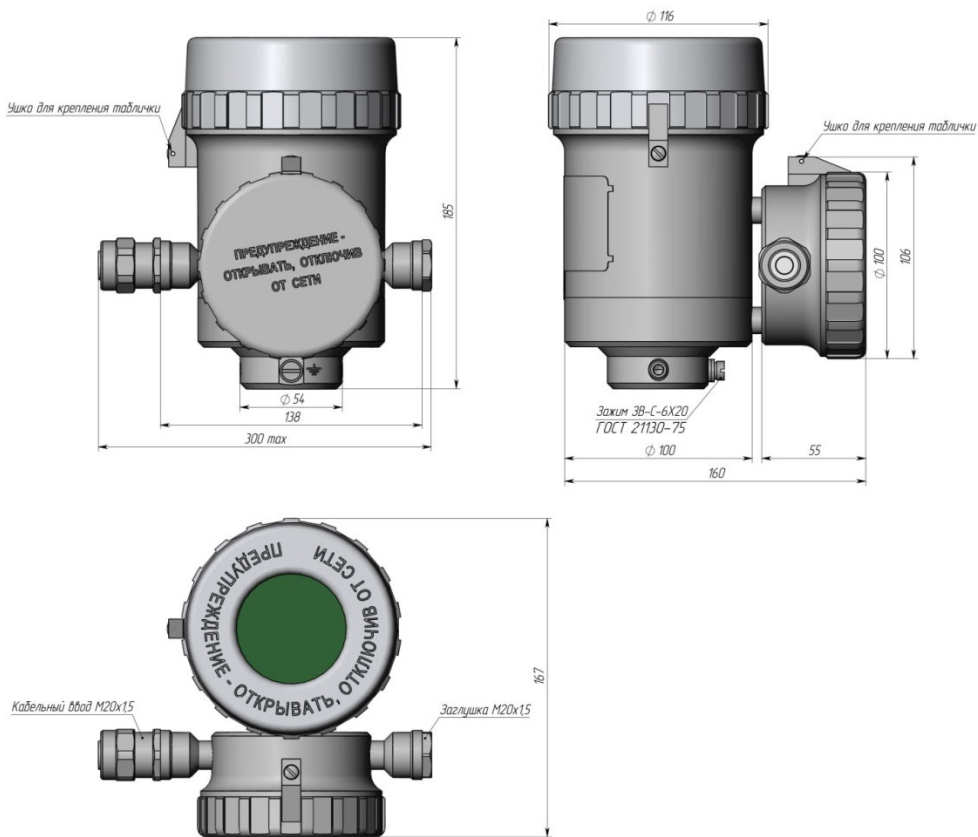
Габаритные и установочные размеры корпуса из нержавеющей стали блока электронного преобразователя. Класс безопасности ЗН. IP67. Дисплей сверху
